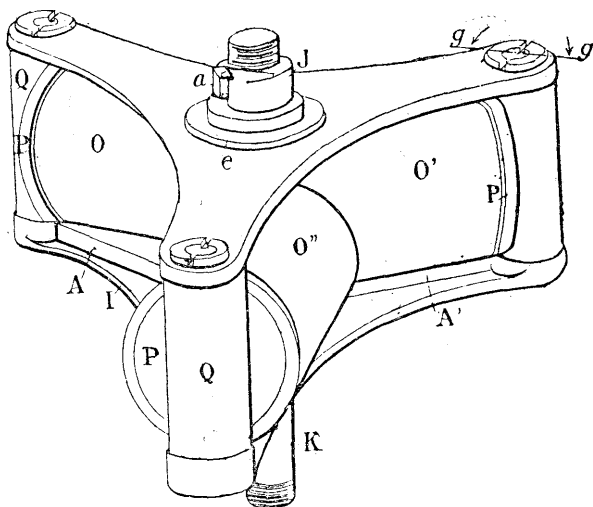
Vue perspective du cadre rotatif de la perceuse « Boyer. »
